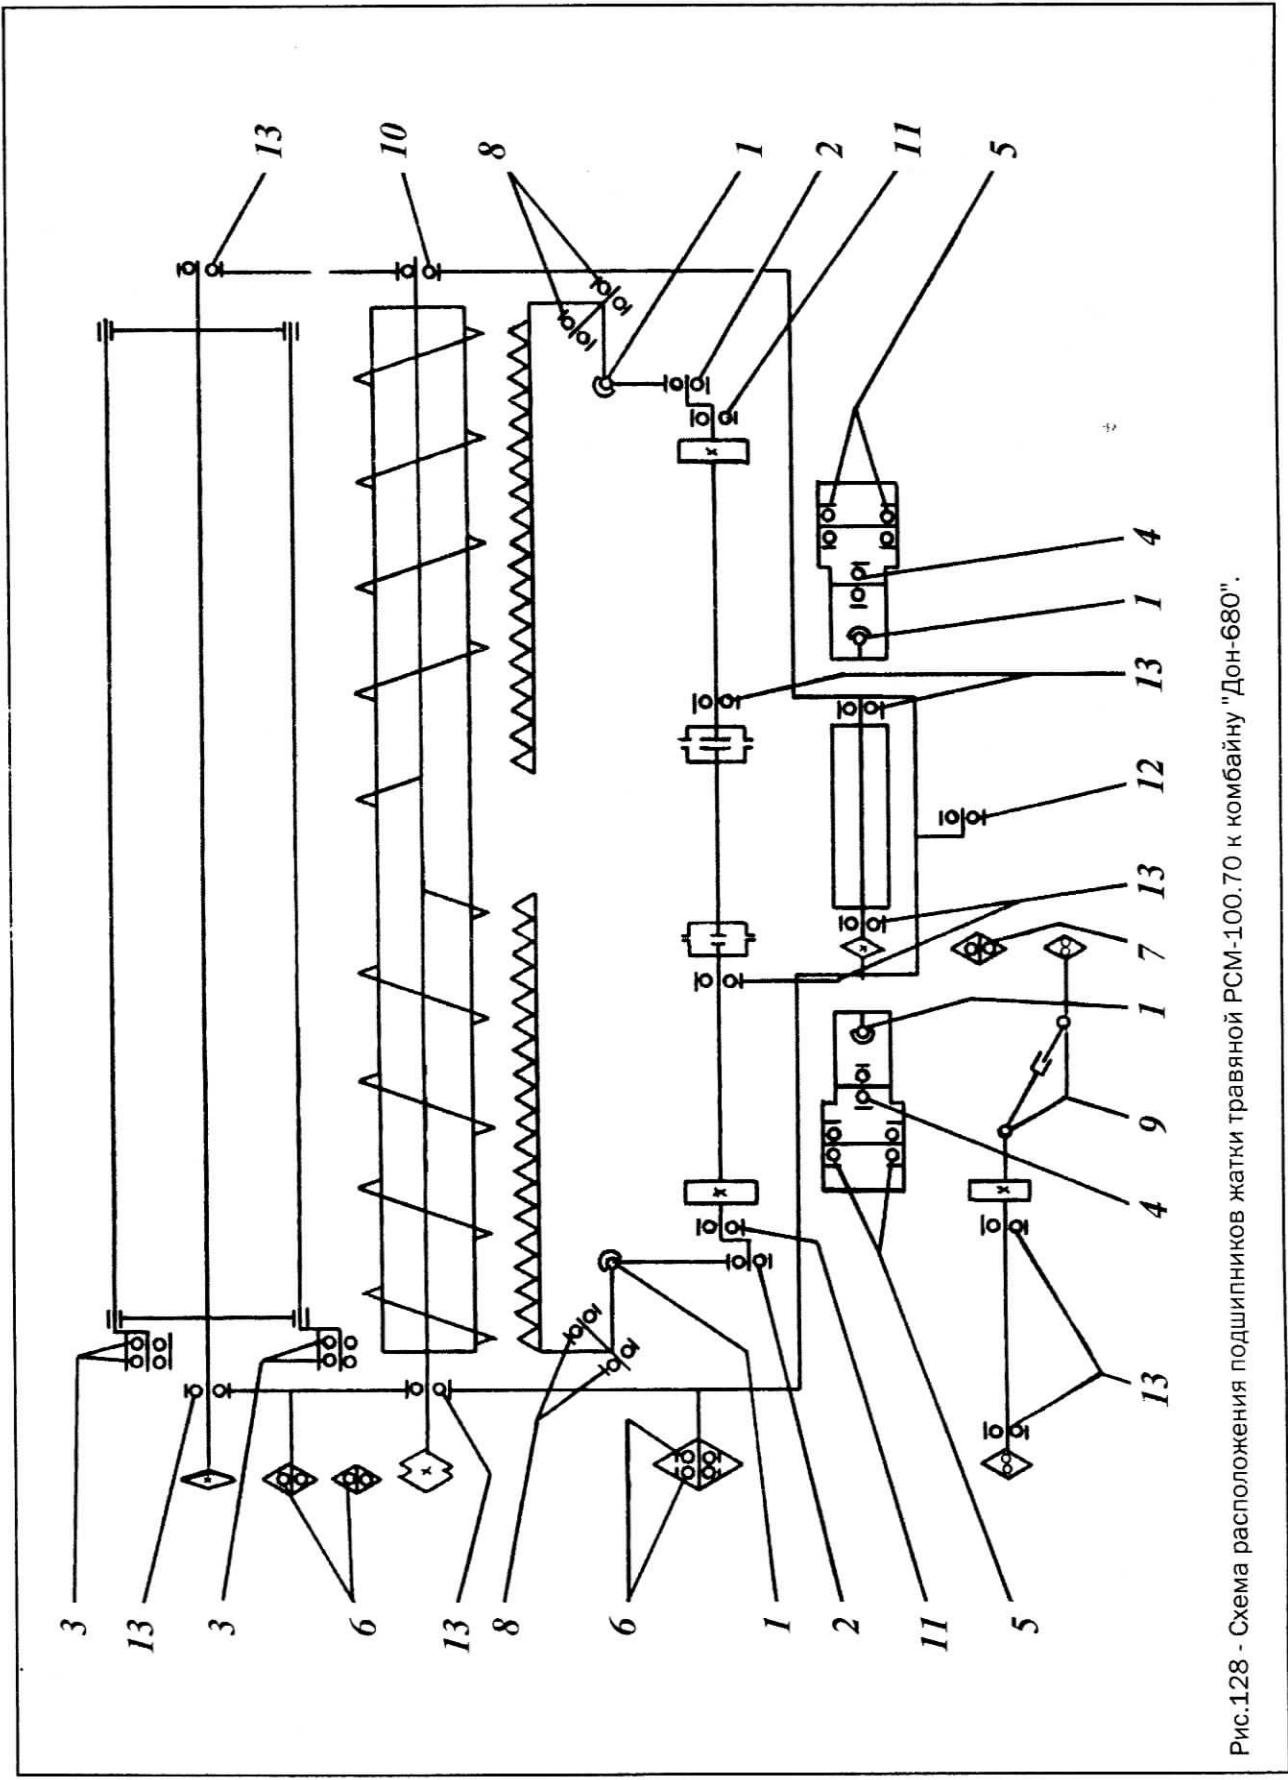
Схема расположения подшипников жатки травяной РСМ-100.70 к комбайну "Дон-680".
